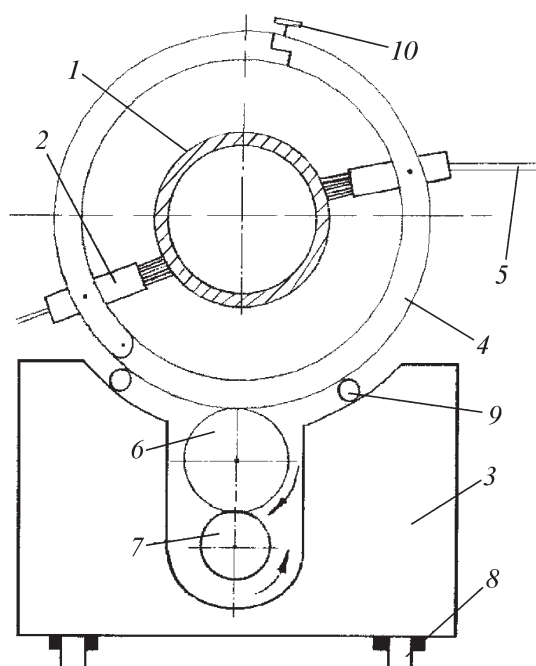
Технологическая схема упрочняющей обработки сварных швов трубопроводов
